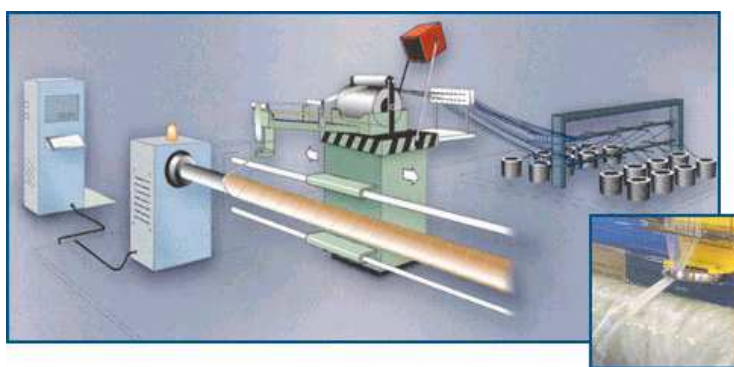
Ilustração da máquina de bobinagem filamentar horizontal (www.saint-gobain-vetrotex.com.br/process_filwind.htm).
